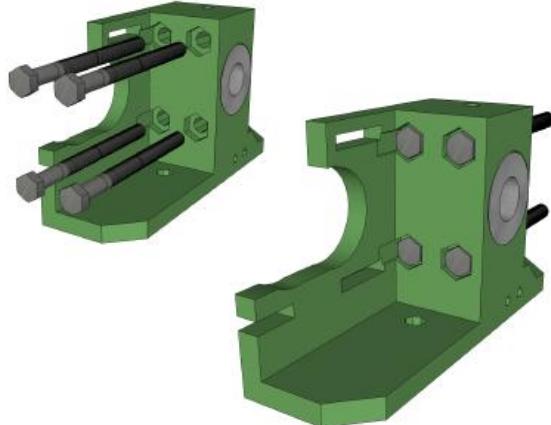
Ensamblado del cuerpo del extrusor (paso 3)
